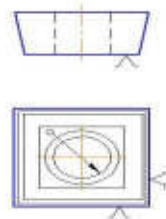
Схема базирования и закрепления сменных пластин.
